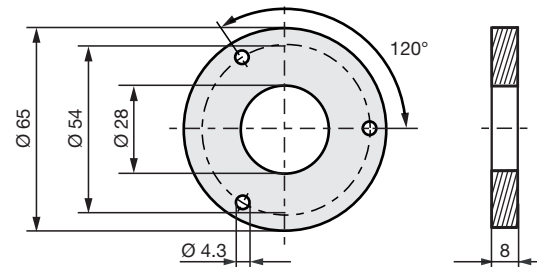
Sonderzubehör BTL-P-1028-15R
